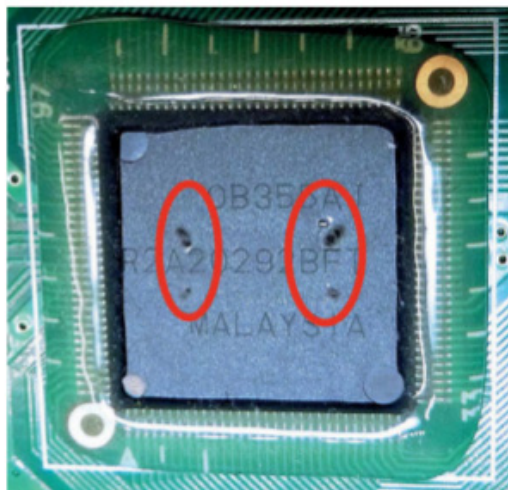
Détail d'un circuit R2A20292BFT (défectueux) soudé et protégé par colle souple
